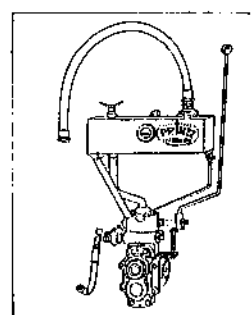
Steuerhebel für Pflugbetrieb, Blockierung am Steuerhebel gelöst, 2 Höchstdruckschlürche für doppelwirkenden hydraulischen Druckzylinder.
